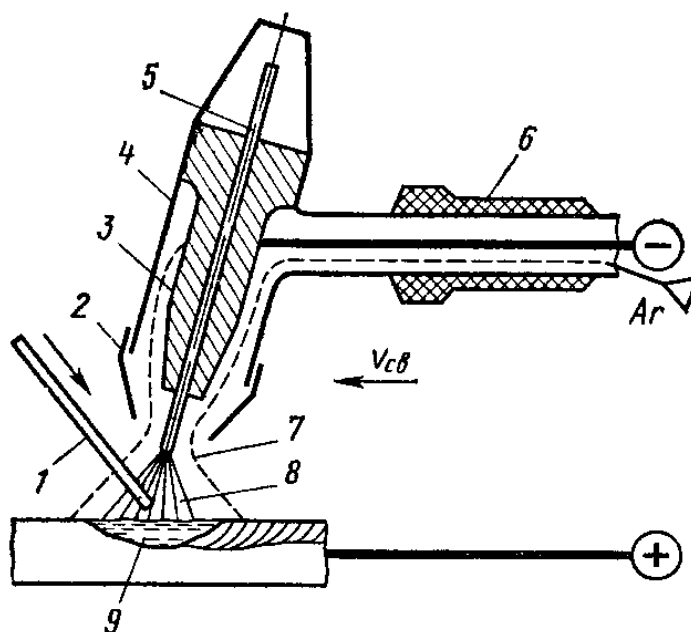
Схема аргонодуговой сварки стали вольфрамовым электродом: 1 –присадочный стальной пруток или проволока, 2 – сопло; 3 – окоподводящий мундштук; 4 – корпус горелки; 5 – плавящийся вольфрамовый электрод; 6 – рукоять горелки; 7 – атмосфера аргона; 8 – сварочная дуга; 9 – ванна расплавленного металла
